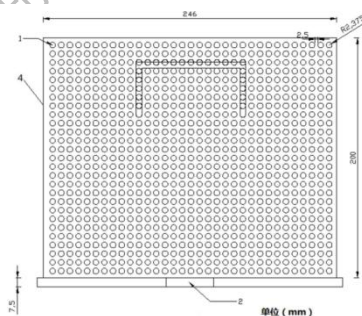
出浆量筒（尺寸单位：mm）
